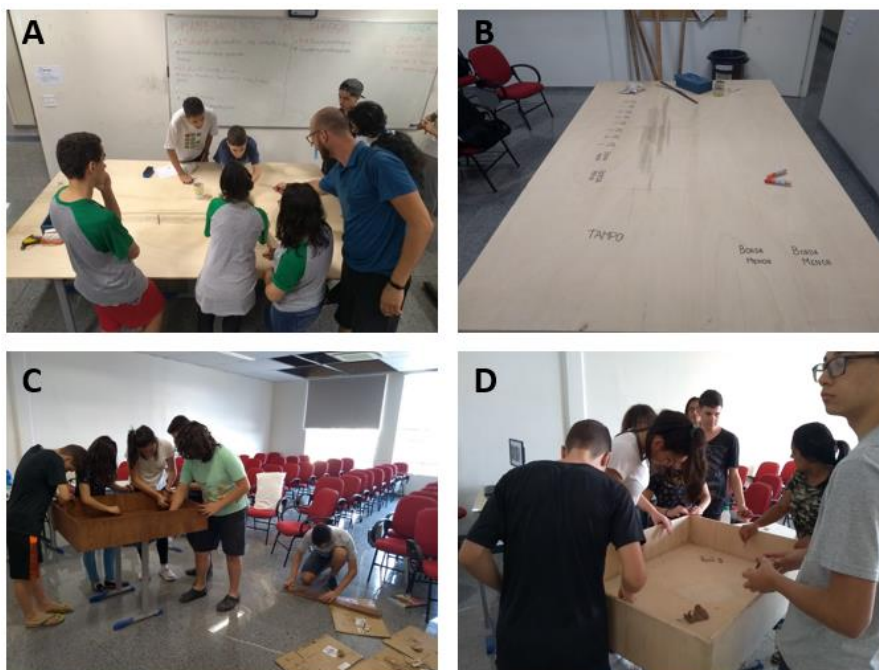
Etapas de planificação e montagem da estrutura da mesa. A: planificação da estrutura, B: plano da mesa planificado, C: envernizamento do tampo da mesa e D: lixamento da estrutura da mesa.
